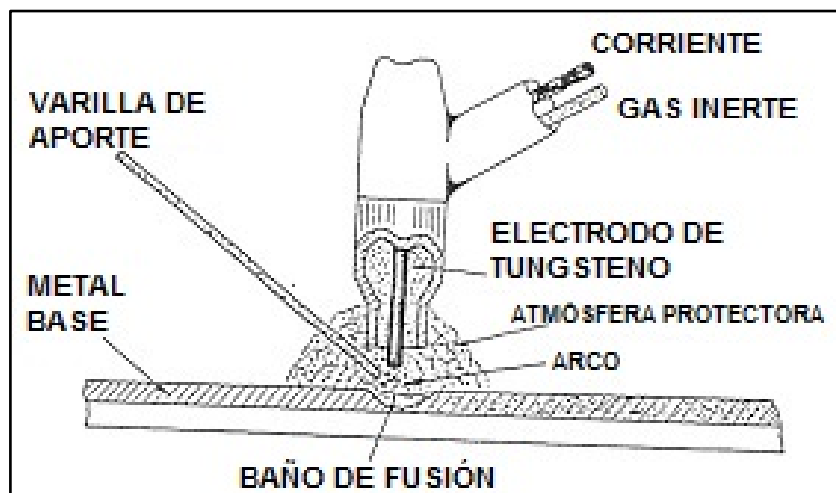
Soldadura TIG o GTAW para acero inoxidable [12]
